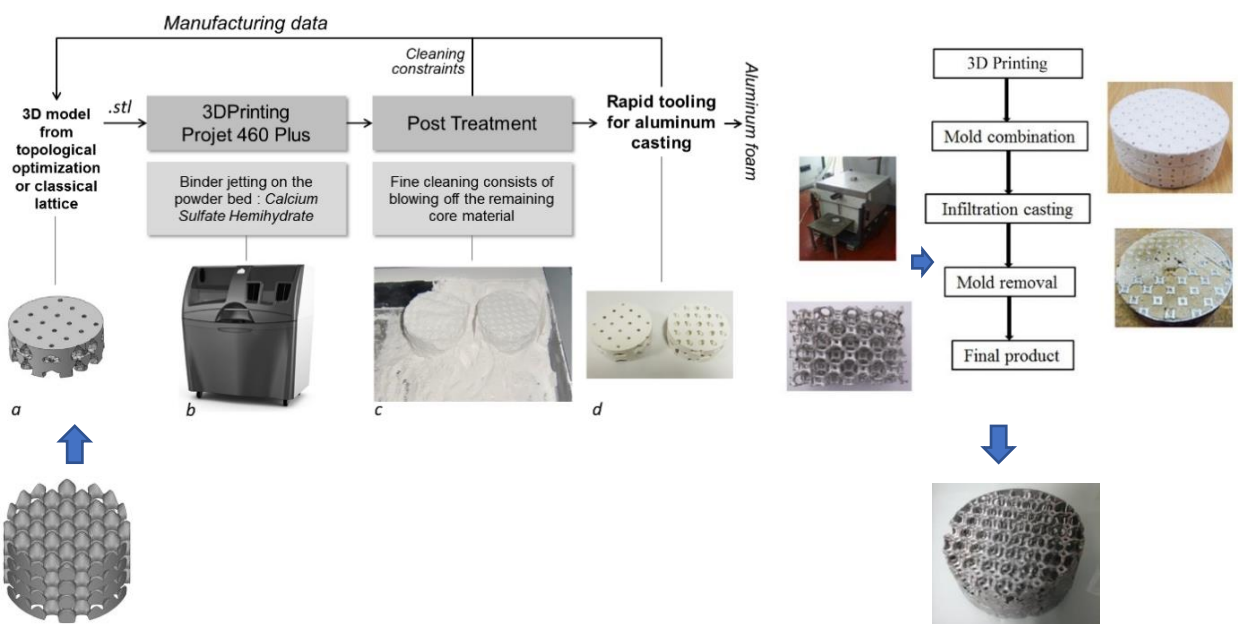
Schéma de principe du moulage de la mousse à cellules ouvertes. Moule en plâtre par impression 3D et procédé de fabrication utilisant le moulage par infiltration
